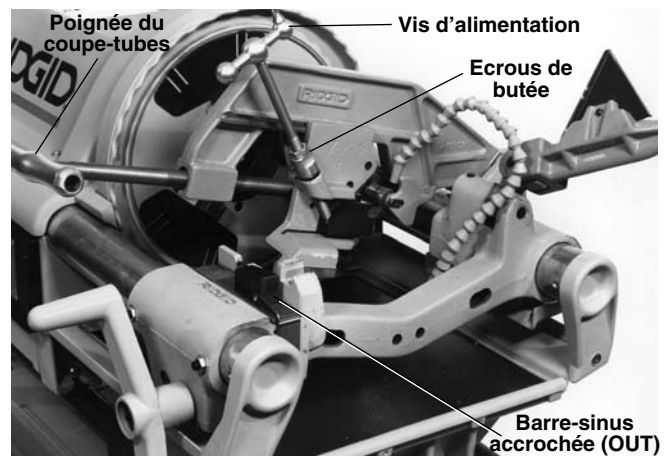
Coupe-tubes pour PVDC installé. (Montré sans tête de filière pour raisons de clarté uniquement.) La tête de filière doit IMPERATIVEMENT être installée et en position RELEVÉE lors de l'utilisation du coupe-tubes 766.
